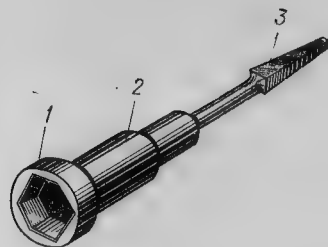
1 — головка; 2 — рабочая часть; 3 — хвостовик
